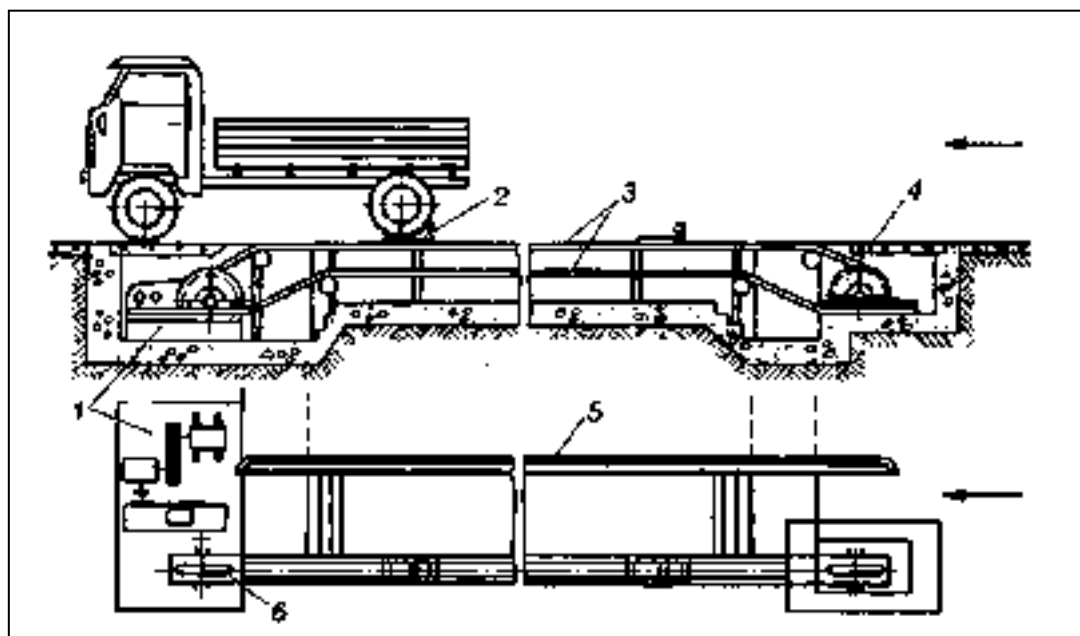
Толкающий конвейер: 1 — приводная станция; 2 — толкающая тележка; 3 — цепи; 4 — натяжная станция; 5 — направляющая; 6 — звездочка
